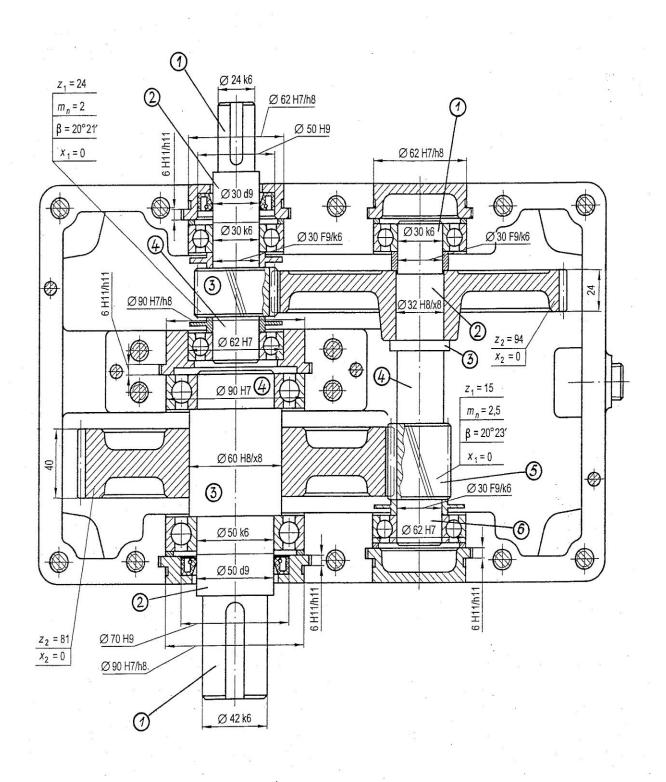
Цилиндрический двухступенчатый соосный зубчатый редуктор с цилиндрическими концами тихоходного и быстроходного вала и с шариковыми радиальными однорядными подшипниками, используемыми в качестве опор валов [I] (к примеру 2.15)
